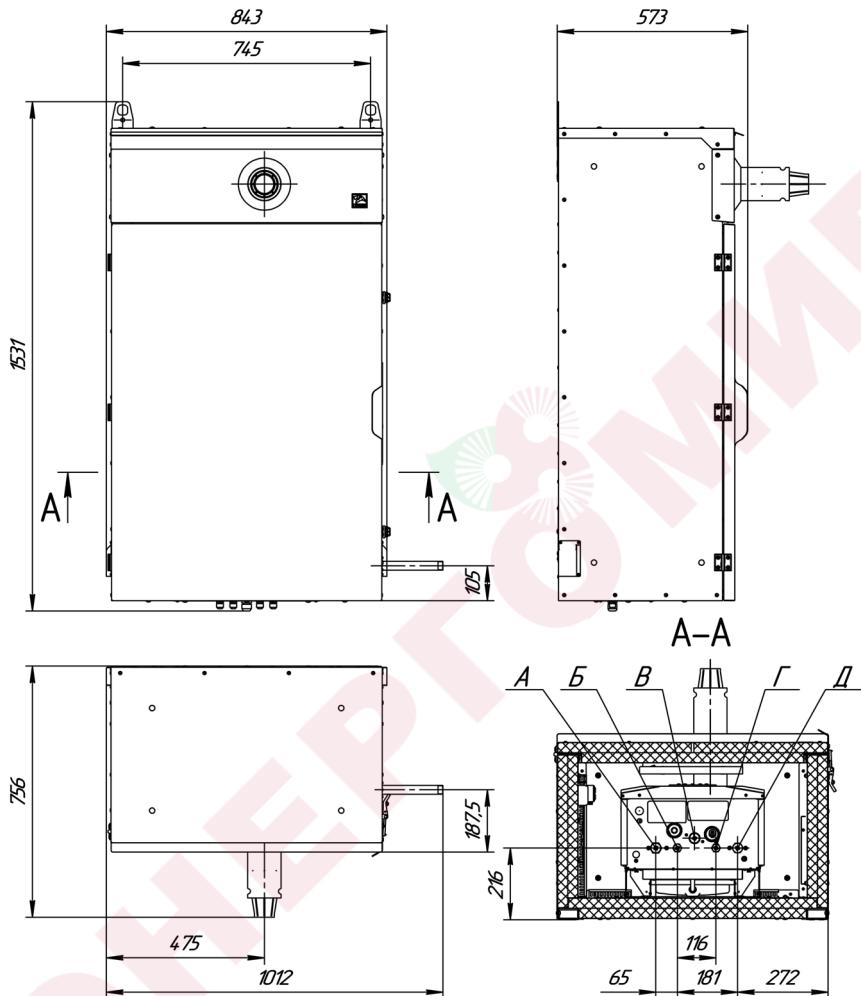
Габаритные и присоединительные размеры котлов Prime-ST26...32; Prime-ST26...32НО
